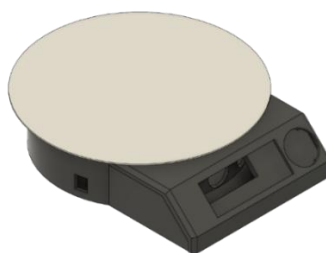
Carcasa realizată în Fusion 360, asamblată - prezentând o vedere generală a designului final.
